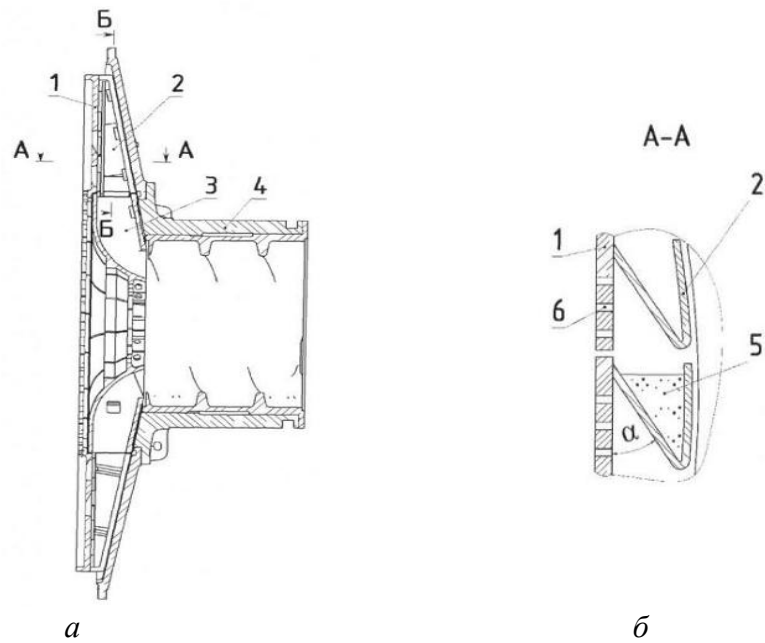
Розвантажувальний пристрій: *а* – схема, основний розріз; *б* – переріз А-А:
